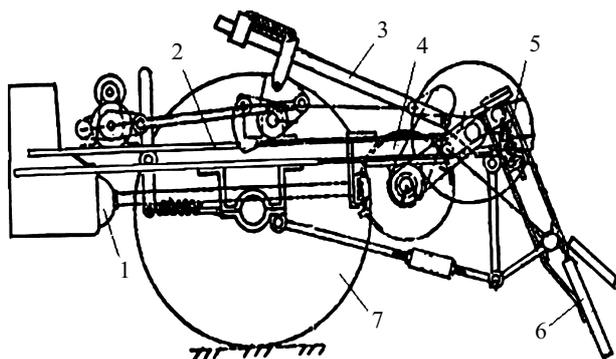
Схема копателя Симса (Великобритания): 1 — привод; 2 — рама; 3 — регулировочный стержень; 4 — коленчатый вал; 5 — предохранительное устройство; 6 — рабочие органы; 7 — колесо
